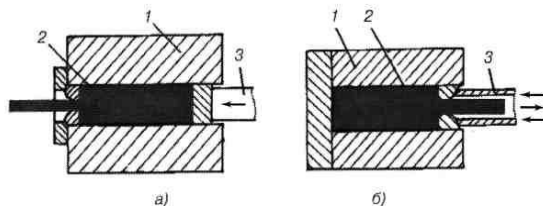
Схема прессования: а — прямое; б — обратное; 1 — матрица; 2 — прессуемая заготовка (изделие); 3 — пуансон
